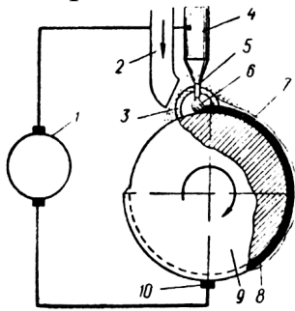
Схема наплавлення під шаром флюсу:
